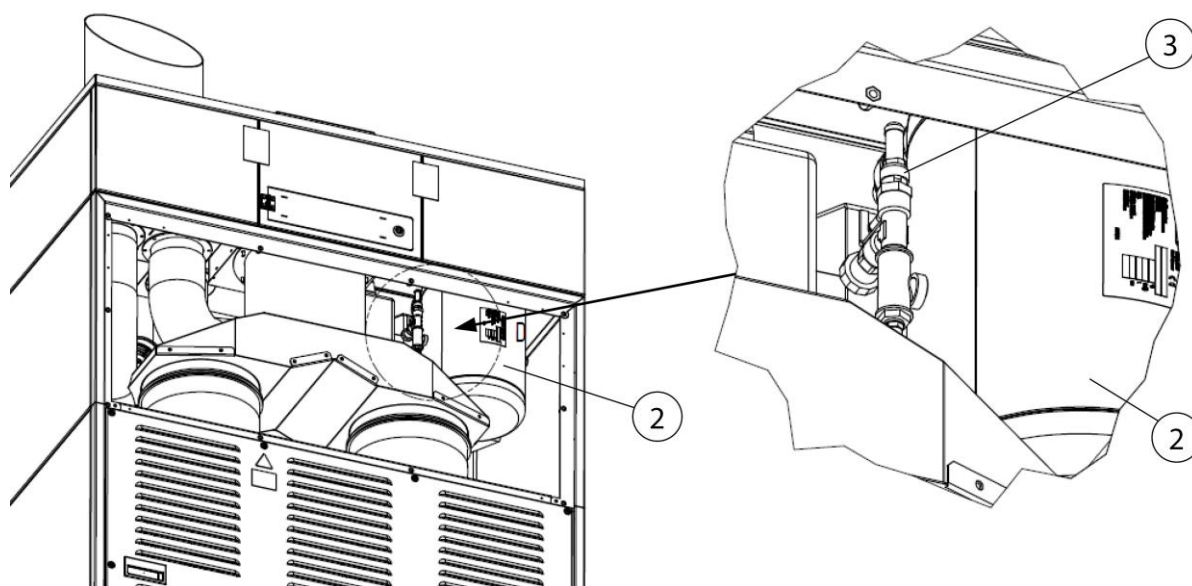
Accès à la soupape de sûreté pour air comprimé
